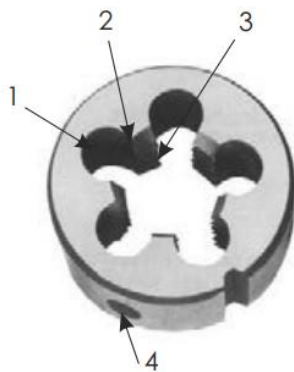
Зовнішній вигляд плашки: 1 – канавка для відведення стружки; 2 – забірна частина (для нарізання неповного витка); 3 – калібрувальна частина (для нарізання повного витка); 4 – отвір для стопоріння
